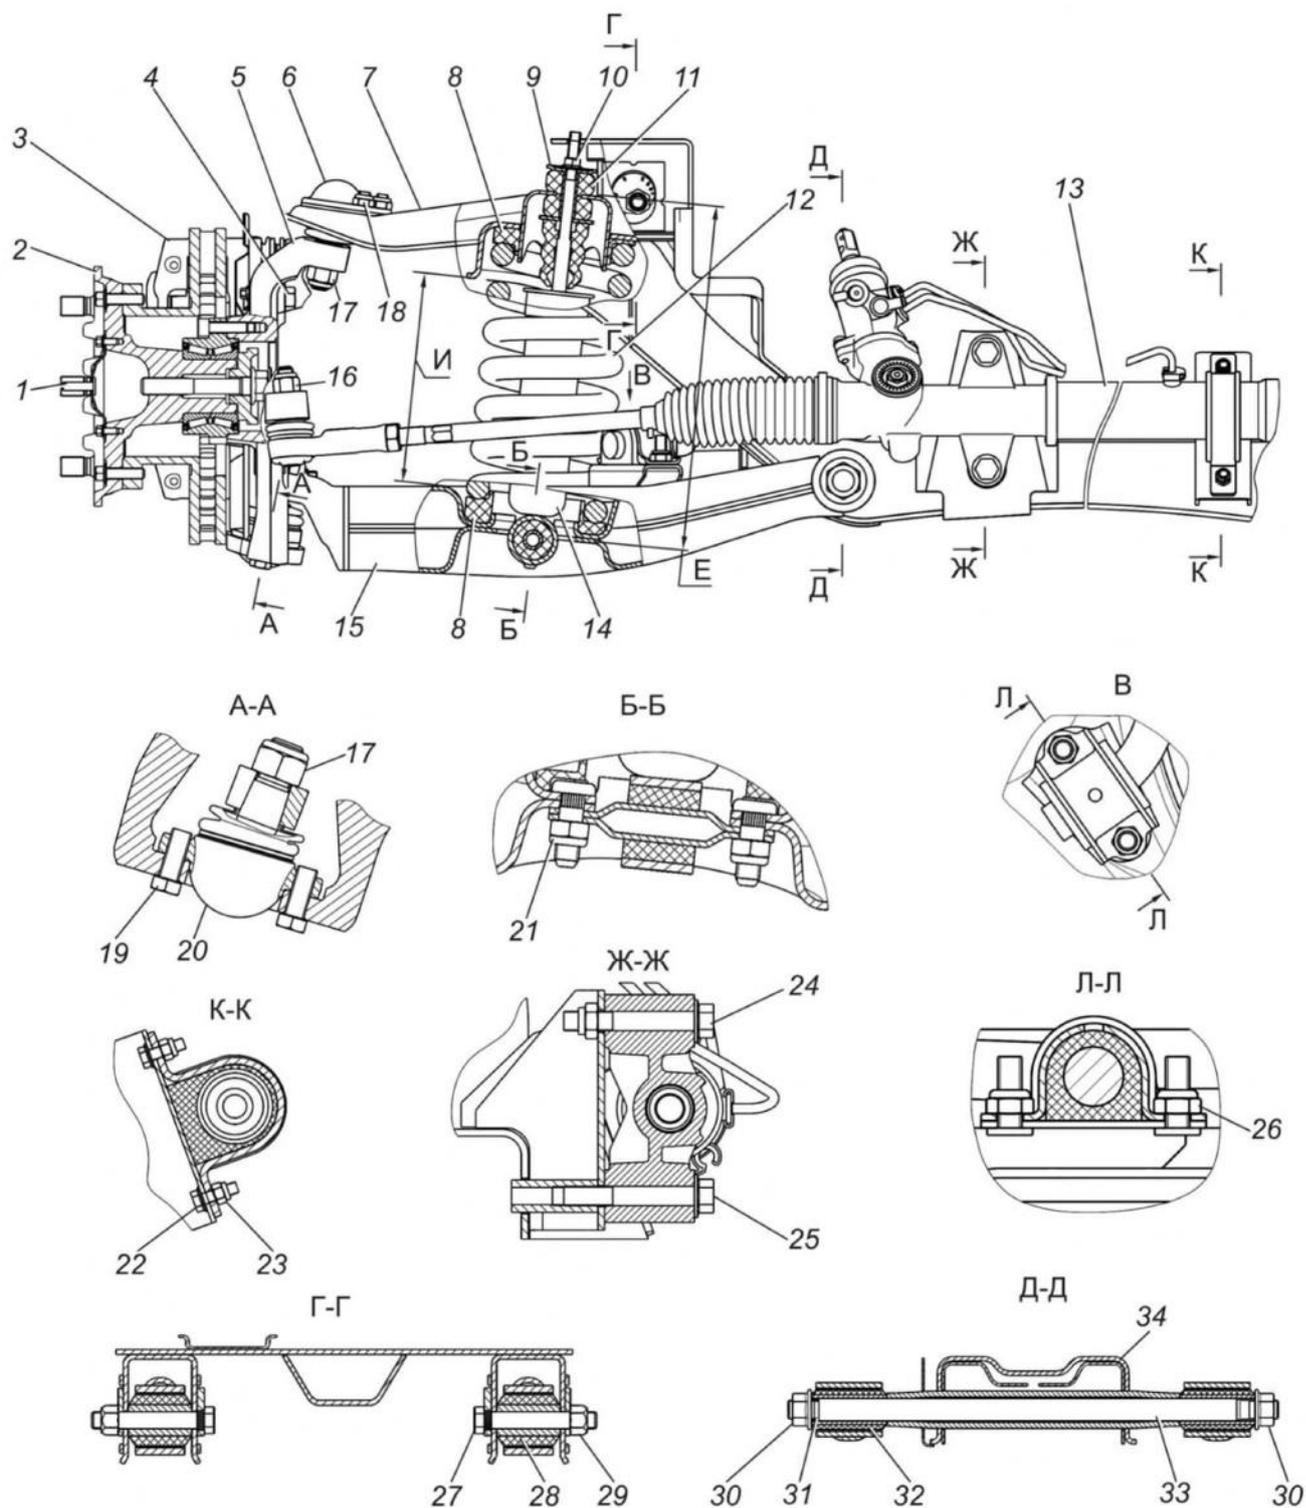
Подвеска передняя с рулевым механизмом: 1 – кронштейн крепления колпака колеса; 2 – стойка со ступицей и тормозным диском; 3 – тормозная скоба; 4 – болт крепления тормозной скобы к стойке; 5 – стойка; 6 – шарнир шаровой верхней; 7 – рычаг верхний; 8 – прокладка пружины; 9 – шайба; 10,16,17,18,21,23,26,29,30 – гайки; 11 – подушка; 12 – пружина; 13 – механизм рулевой; 14 – амортизатор; 15 – рычаг нижний; 19,22,24,25 – болты; 20 – шарнир шаровой нижней; 27 – регулировочный болт в сборе с эксцентриковой шайбой; 28 – сайлентблок верхних рычагов; 31 – втулка; 32 – сайлентблок нижних рычагов; 33 – ось нижних рычагов, 34 – подрамник
